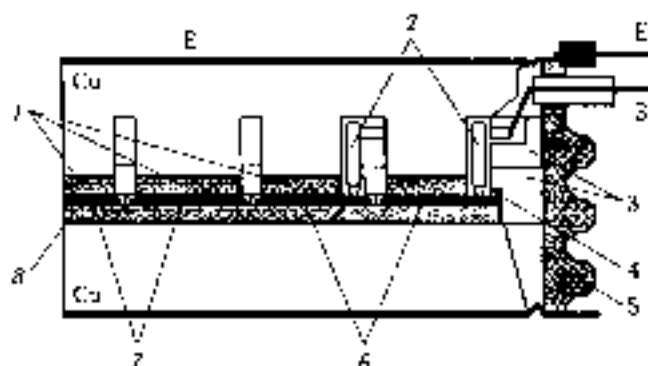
Розріз конструкції IGBT-модуля притискової конструкції: 1 — молибденіві прокладки, 2 — затвор, 3 — сепаратор, 4 — рамка, 5 — керамічний корпус, 6 — чіпи IGBT, 7 — чіпи FRD, 8 — ізолюючий диск
